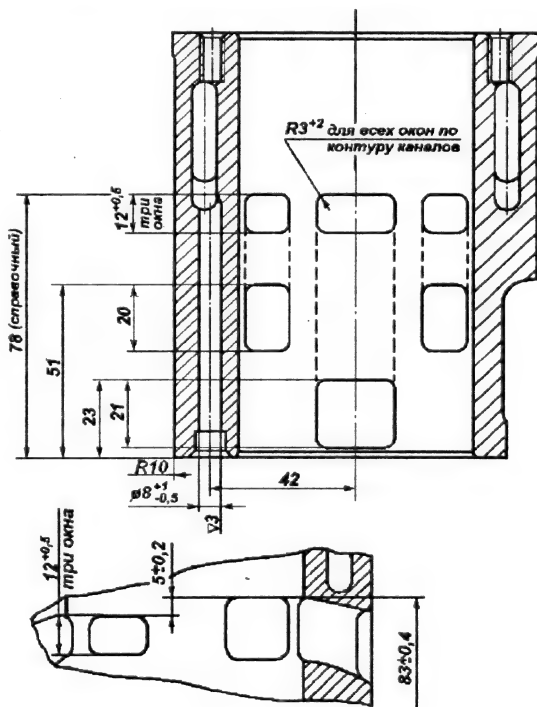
Цилиндр двигателя мотора «Вихрь»
